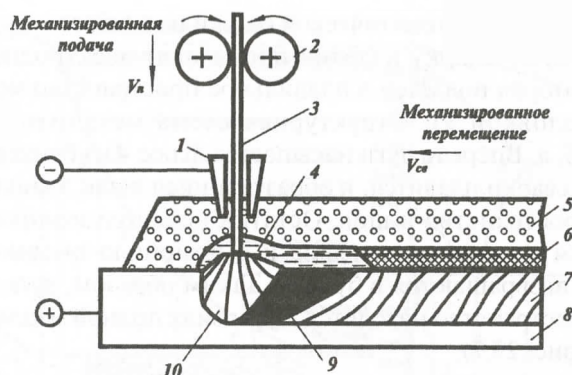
Схема автоматической дуговой сварки под флюсом:
